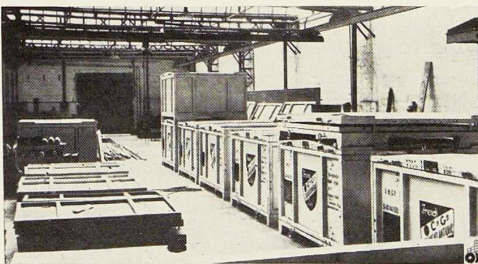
Containers démontables en panneaux en tôle, assemblés par soudure.
